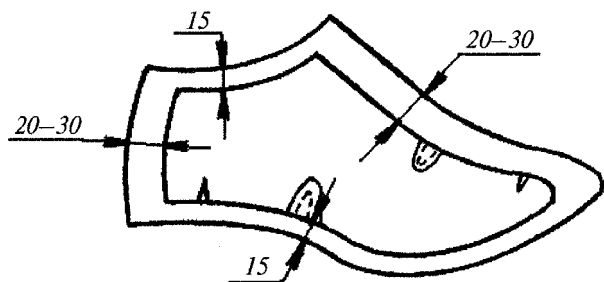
Схема расположения припусков для получения шаблонов из футора
